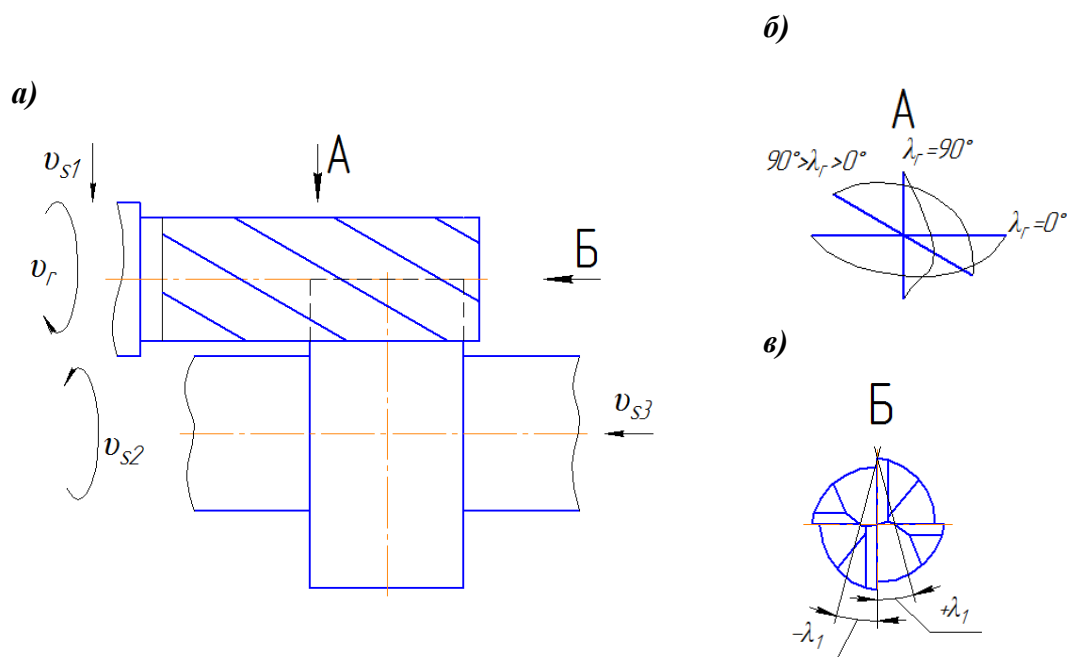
Схема обработки плоской поверхности вращающейся детали вращающимся инструментом (а) и возможные углы наклона режущей кромки на цилиндрической (б) и торцовой (в) поверхностях концевой фрезы
